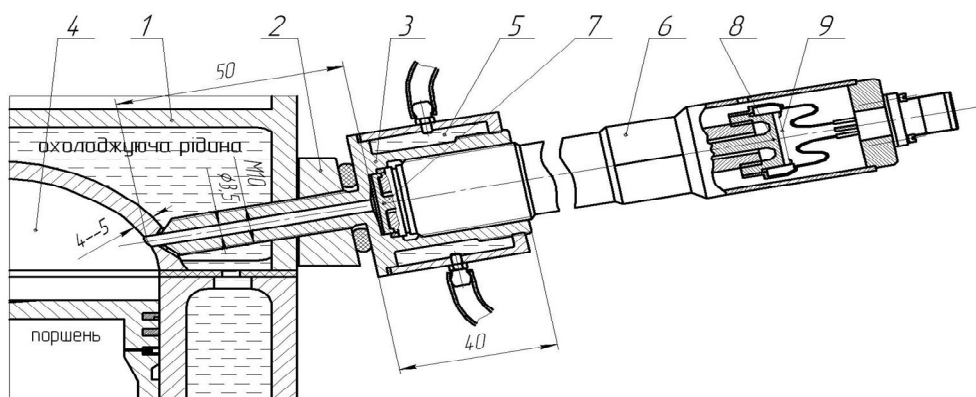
Схема встановлення пристрою для вимірювання тиску в циліндрі двигуна.
